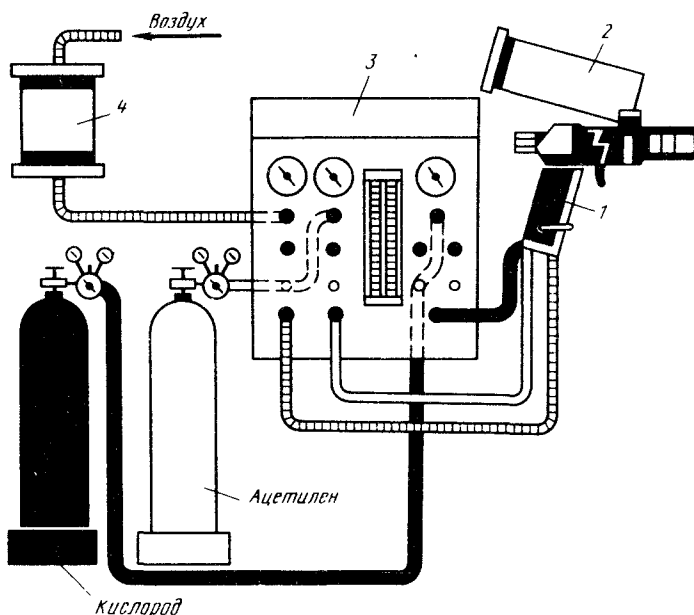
Компоновка установки для газопламенного порошкового напыления
